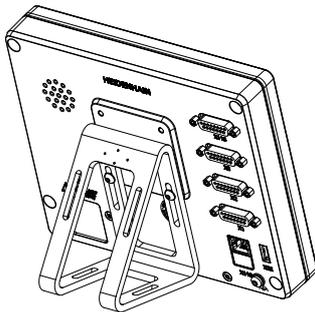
Dispositivo montado en soporte bisagra Duo-Pos
